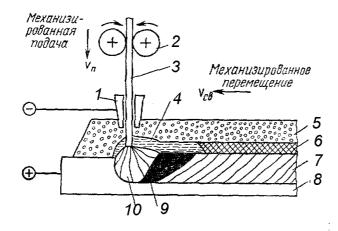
Автоматическая сварка под слоем флюса
